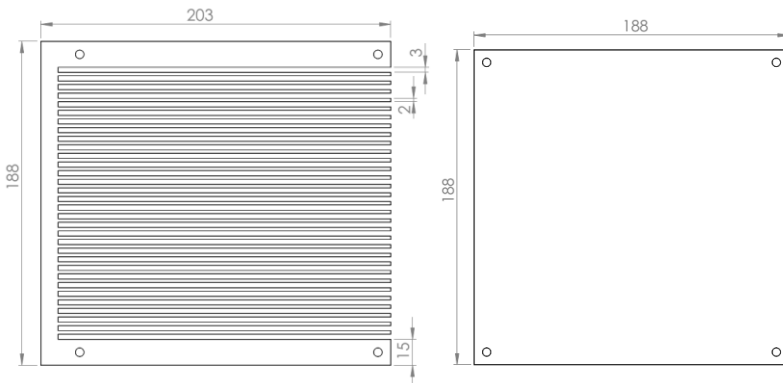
Dimensões das placas usinadas e placas intermediárias.
